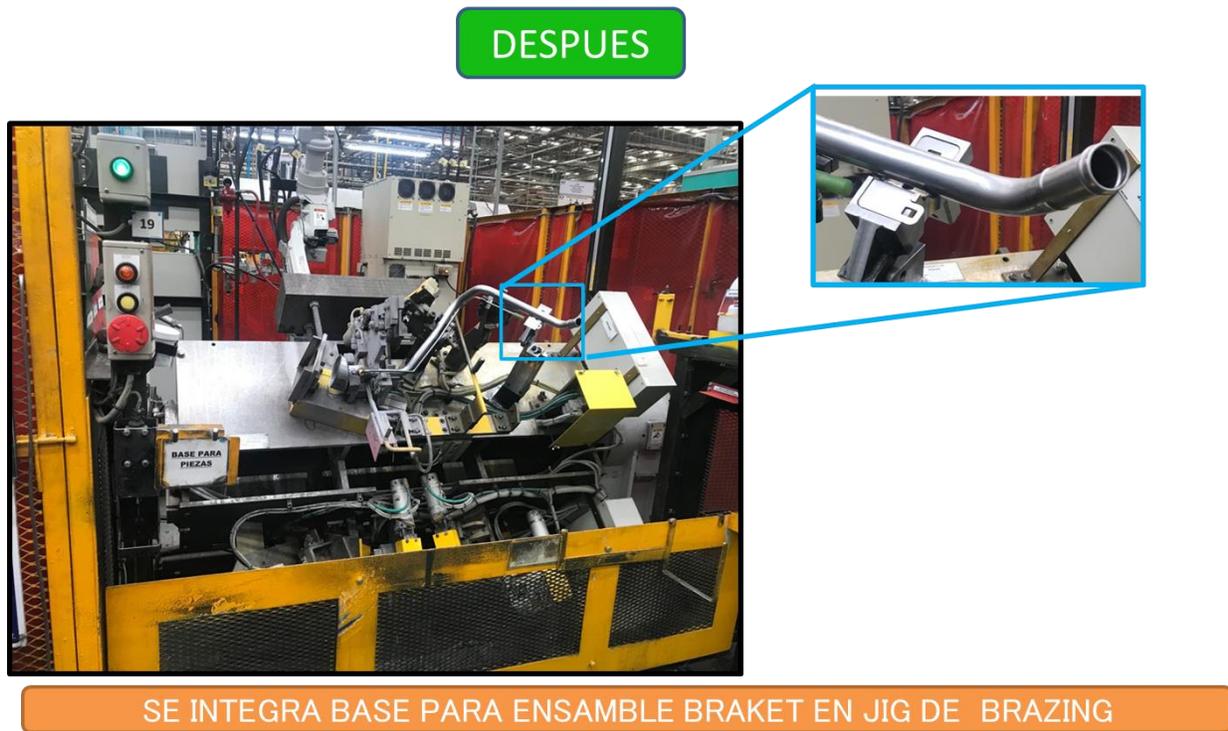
Acoplamiento de base para bracket. Fuente: propia.
